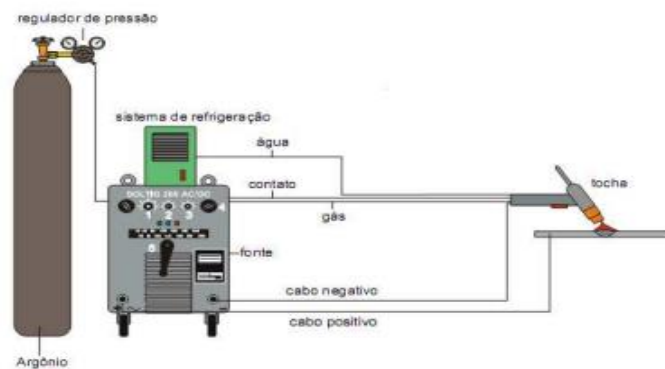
Esquemático do procedimento de soldagem TIG.
